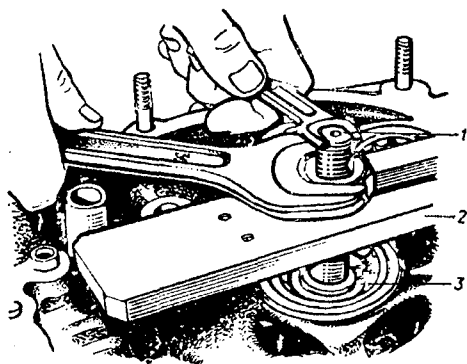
Выпрессовка роликового подшипника шестерни-вала главной передачи: 1 – втулка ведомого вала; 2 – рукоятка; 3 – втулка ведущего вала; 4 – держатель
